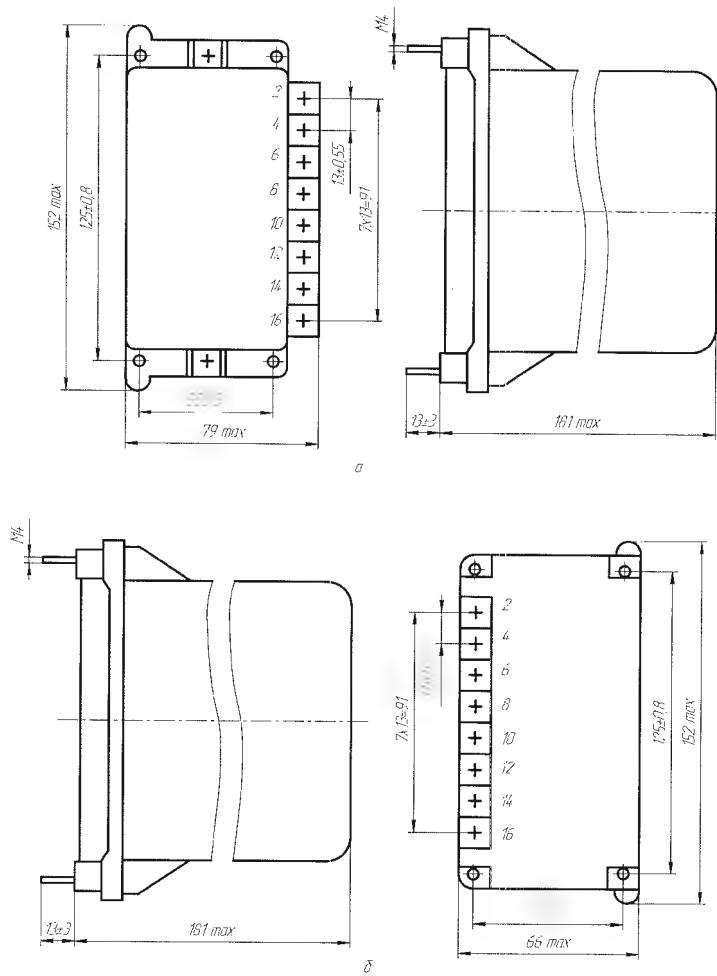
Габаритные, установочные, присоединительные размеры реле РСТ 11М.
